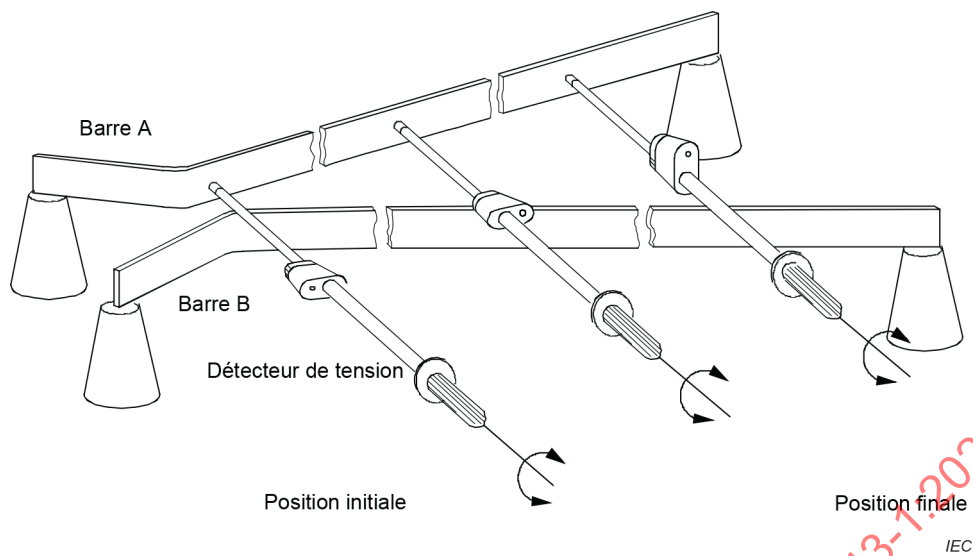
Essai de contraintes transversale et longitudinale (voir 6.3.2.1.2.3)
